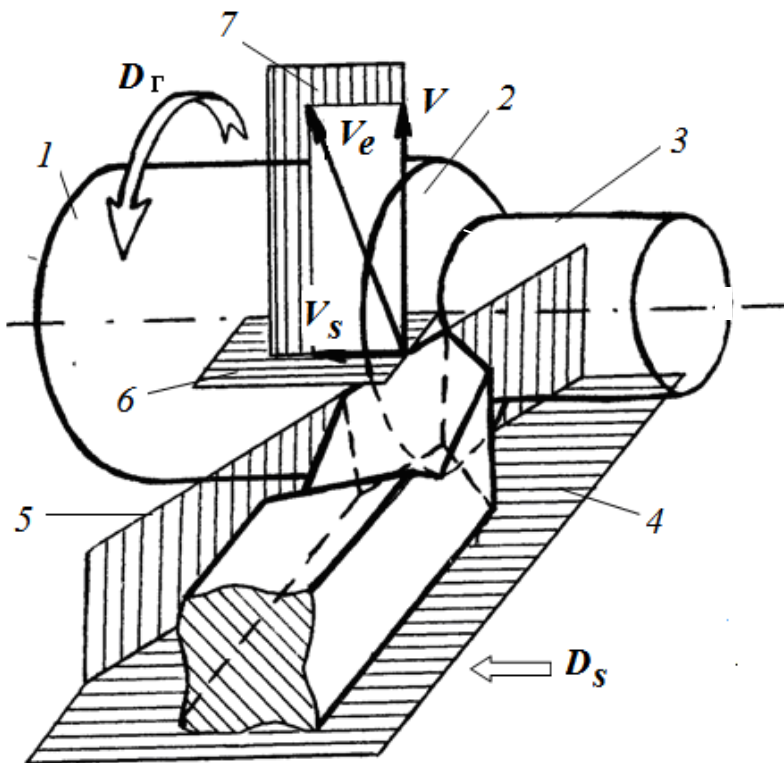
Схема обработки заготовки проходным прямым резцом с основными плоскостями
